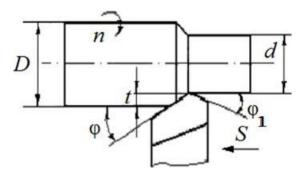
Схема обработки заготовки при определении продольной шероховатости
